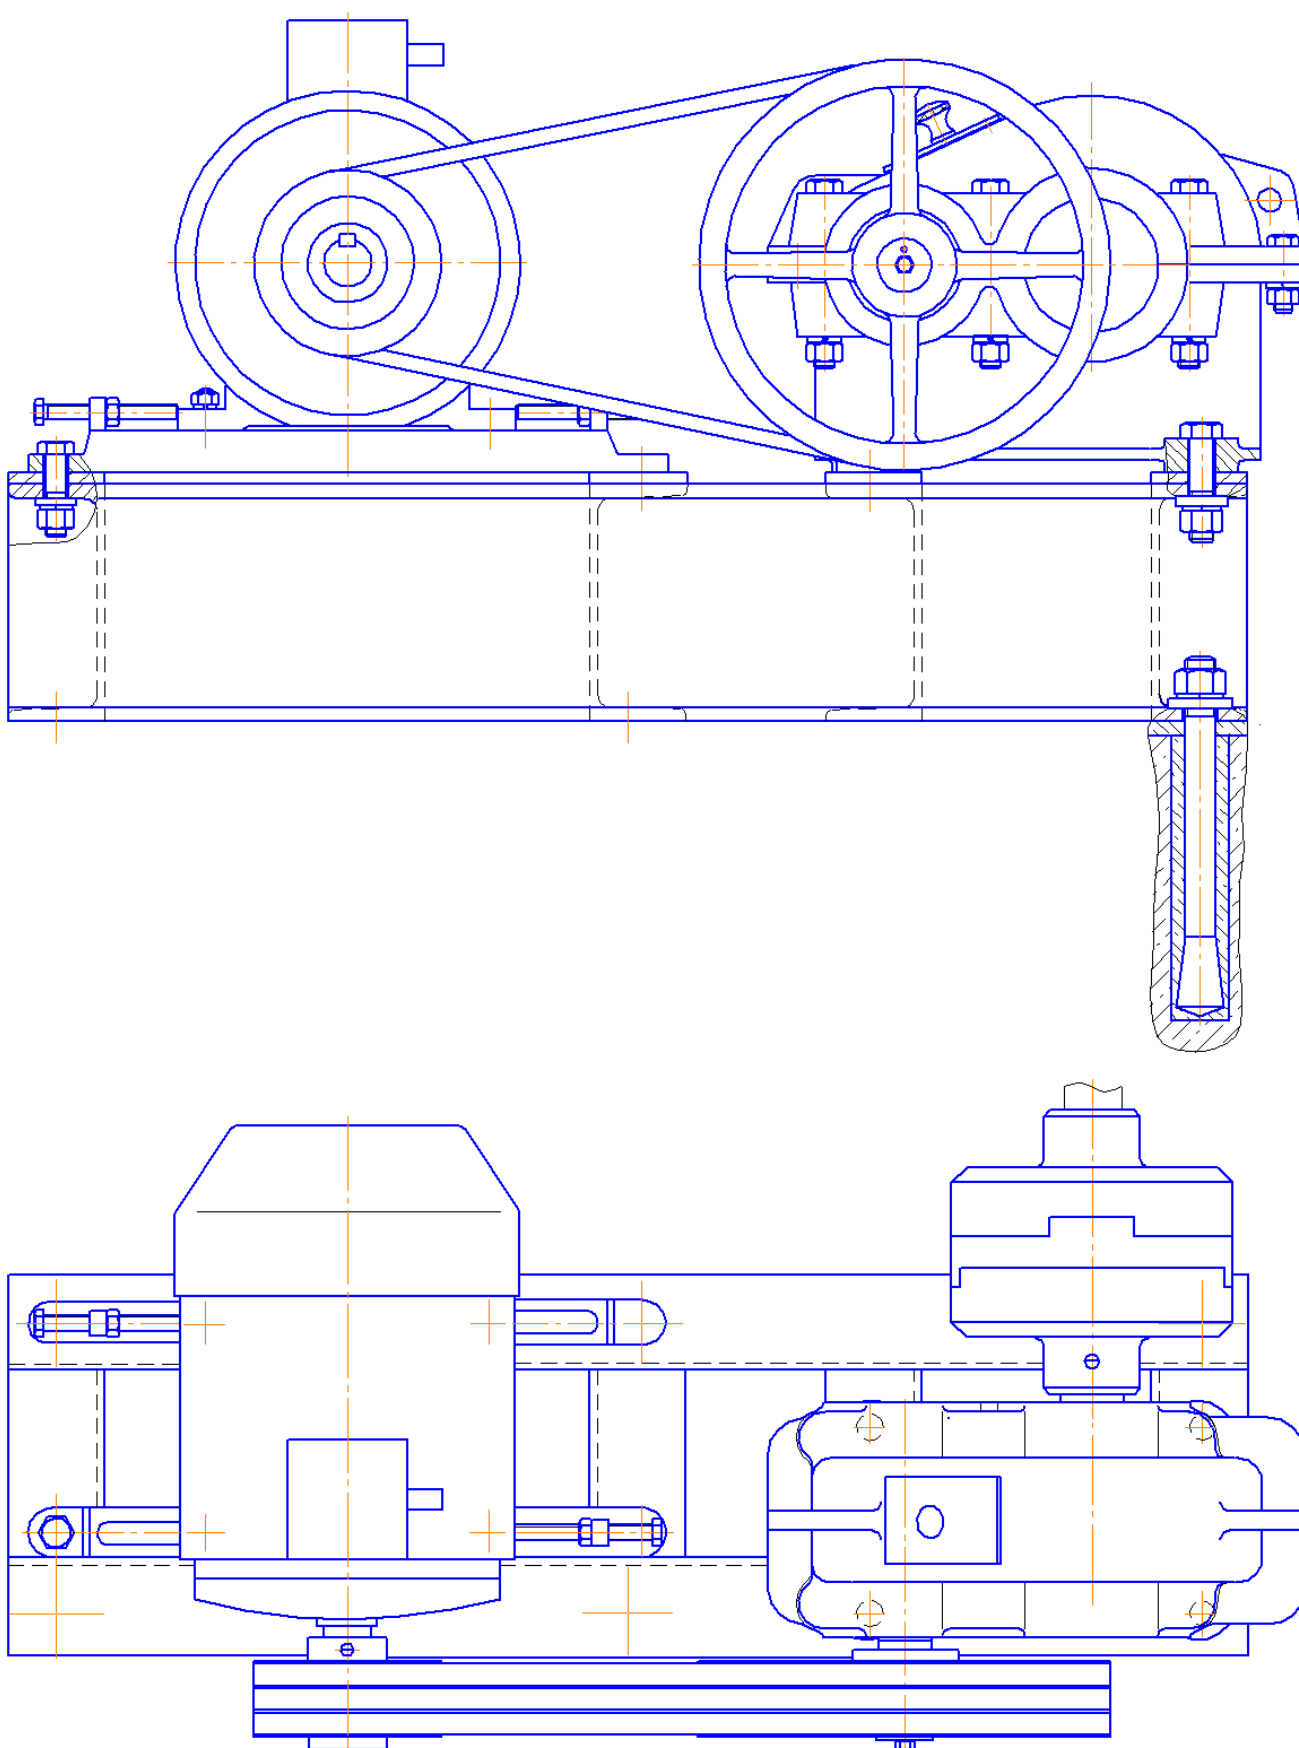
Привод с ременной передачей, редуктором типа 1ЦУ и муфтой кулачково-дисковой
